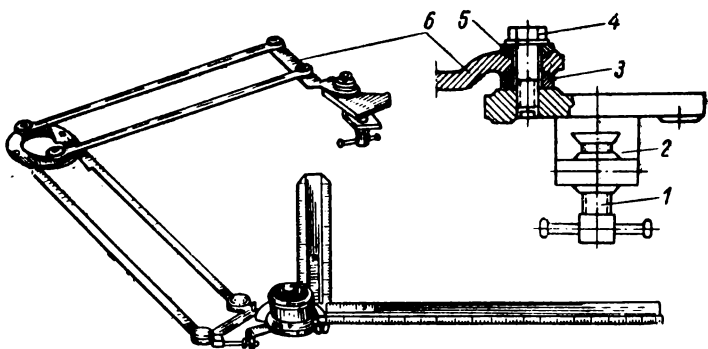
Настольный чертежный прибор ОЗВ-1.
